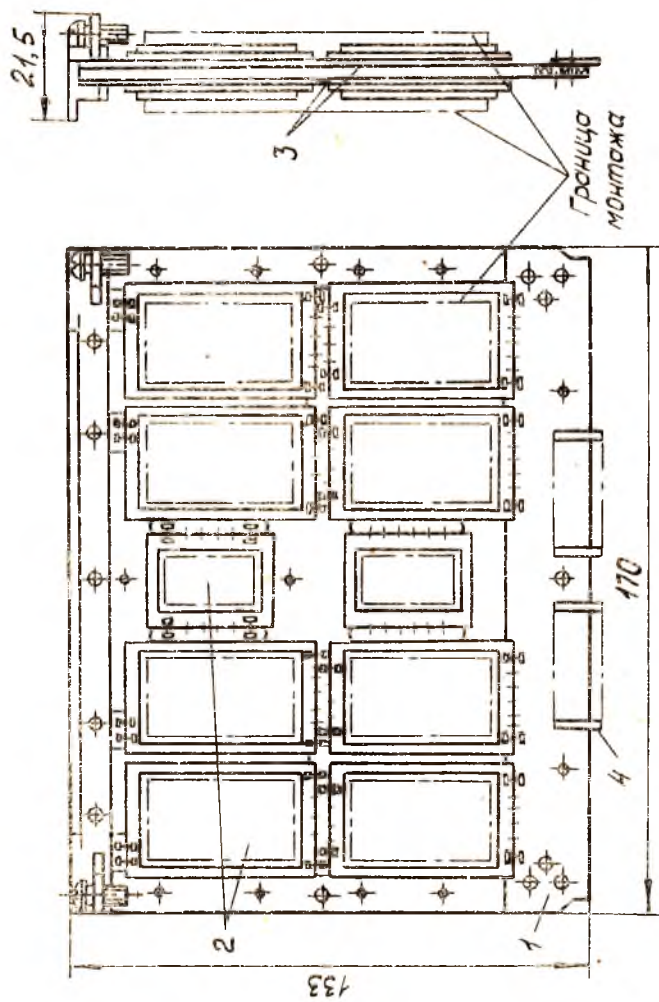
Ячейка герметичного блока МЭА разъемной конструкции: 1 — печатная плата; 2 — бескорпусные МСБ; 3 — металлические шины — основания; 4 — лепестковый контакт соединителя
